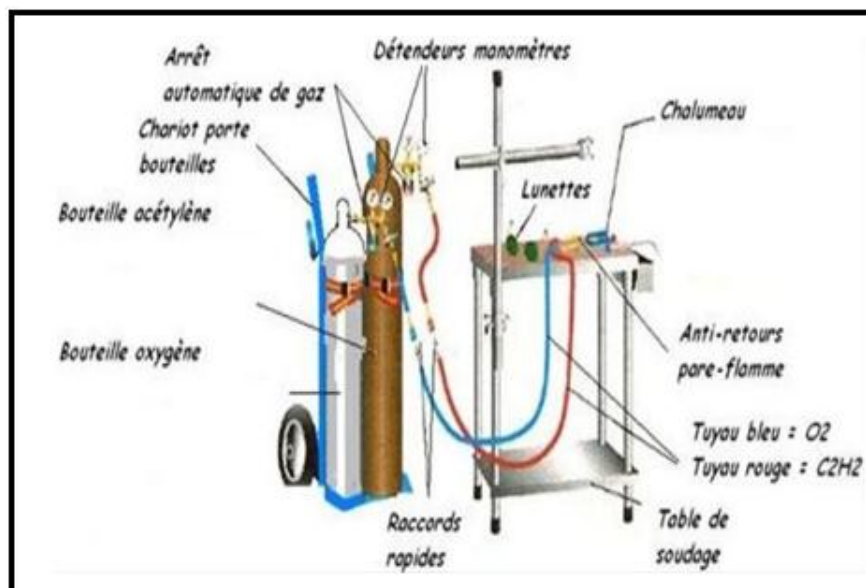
Équipements utilisés pour le soudage oxyacétylénique [8].
